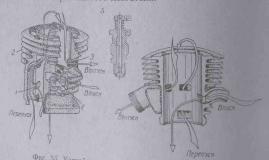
Двигатель мотоциклов М1А и К-125. 1— всасывающий патрубок; 2—продувочные каналы; 3— выхлопной патрубок.
